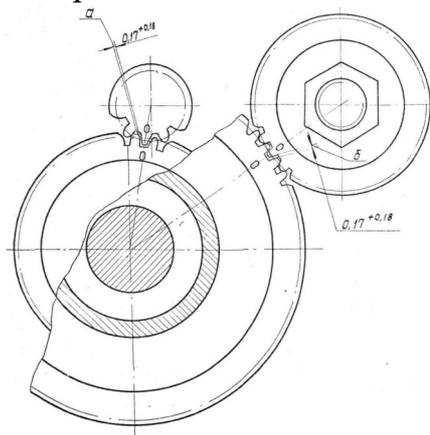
Регулировка размеров «а» и «б» зацепление зубчатых передач редуктора и силовых валов.
